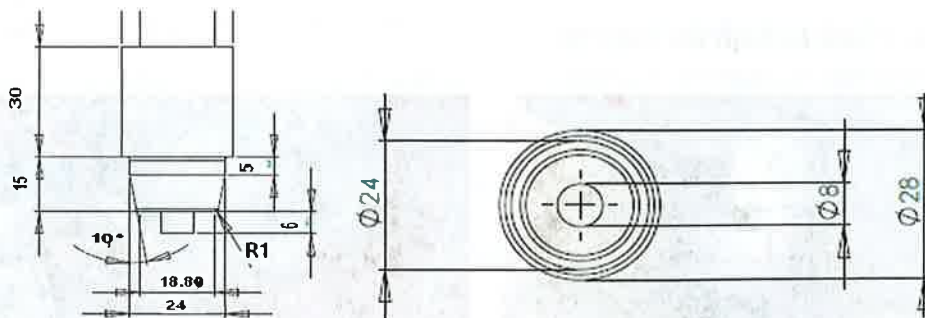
Herramienta B para FSW CIDESI. Dimensiones en mm.
